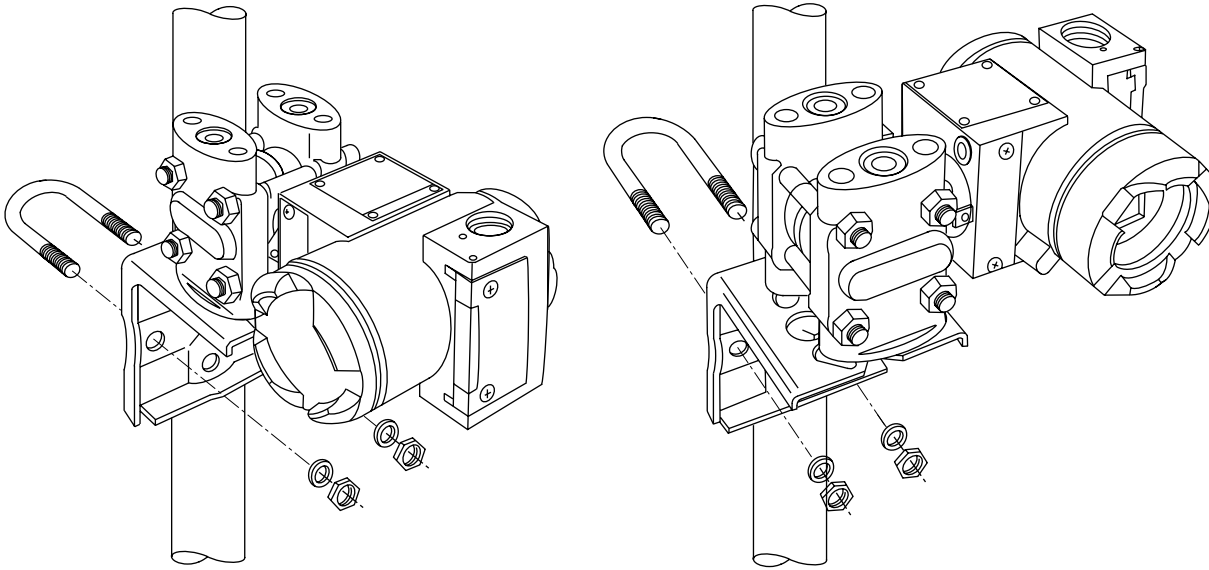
Befestigung mit Montagewinkel am Beispiel Differenzdruck bei senkrechten Wirkdruckleitungen
